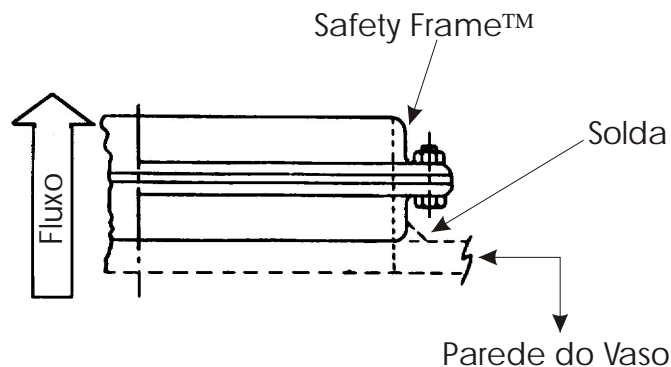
VENT - SAF™ Montagem Soldada
